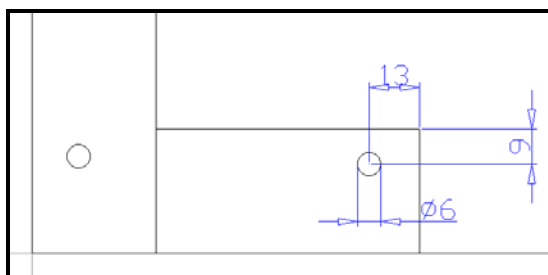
Posição dos furos da cantoneira inferior do suporte cilindro (detalhe 2).
